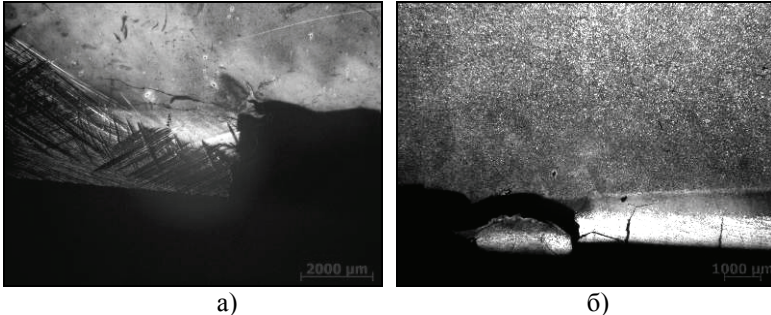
Общий вид дефектов в металле ободьев колес. а) из стали марки Т, б) из стали марки 2
